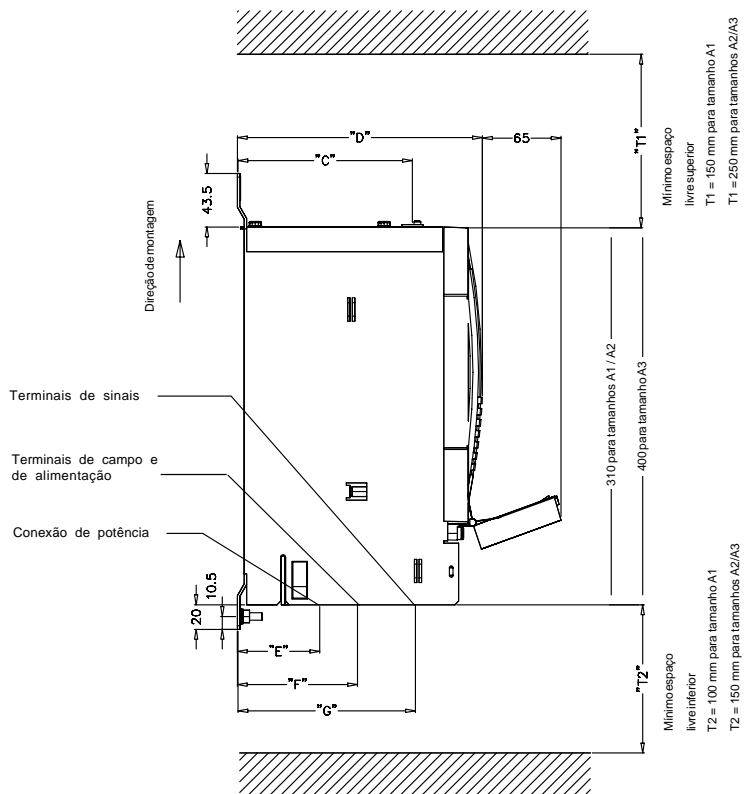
/1: Desenho dimensional dos módulos A1, A2, A3
